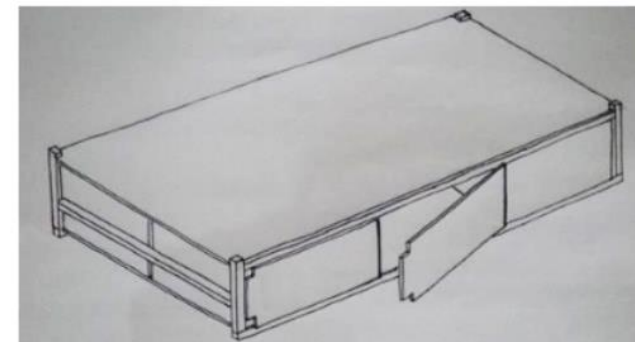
Boceto de camas con puertas plegables y sistema de canaleta
